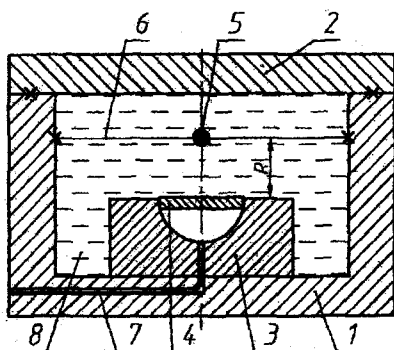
Штамповка крупногабаритных заготовок: 1 – корпус бассейна; 2 – крышка корпуса, прикрепляемая к корпусу стяжными болтами; 3 – матрица; 4 – деформируемая заготовка; 5 – БВВ (заряд); 6 – устройство крепления заряда; 7 – канал для выхода воздуха; 8 – вода
